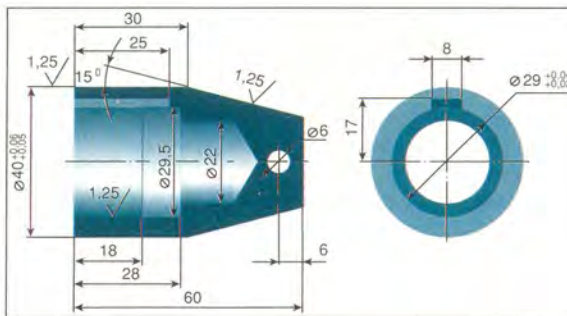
Оправка для центрирования сальника с держателем по коленчатому валу двигателя ВАЗ–2105.
